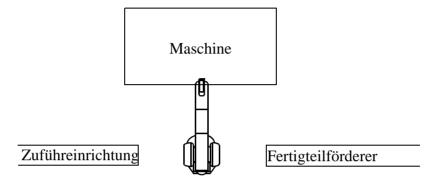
Der Manipulator legt ein Werkstück in die Maschine ein, das anschließend bearbeitet wird.
